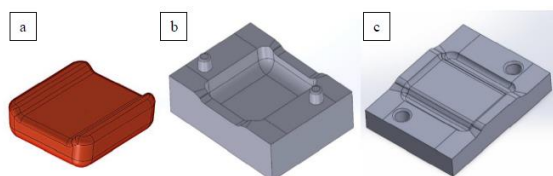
Prototipo de cojín (a), base molde cojín (b), tapa molde cojín (c).
